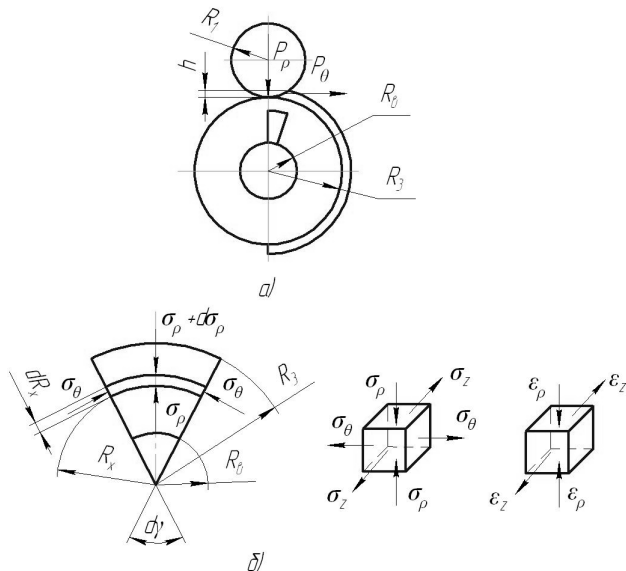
Розрахункова схема для визначення зусилля деформації заготовки шнека: а) схема взаємодії шнека із роликом; б) напружений стан елементарного сектора
